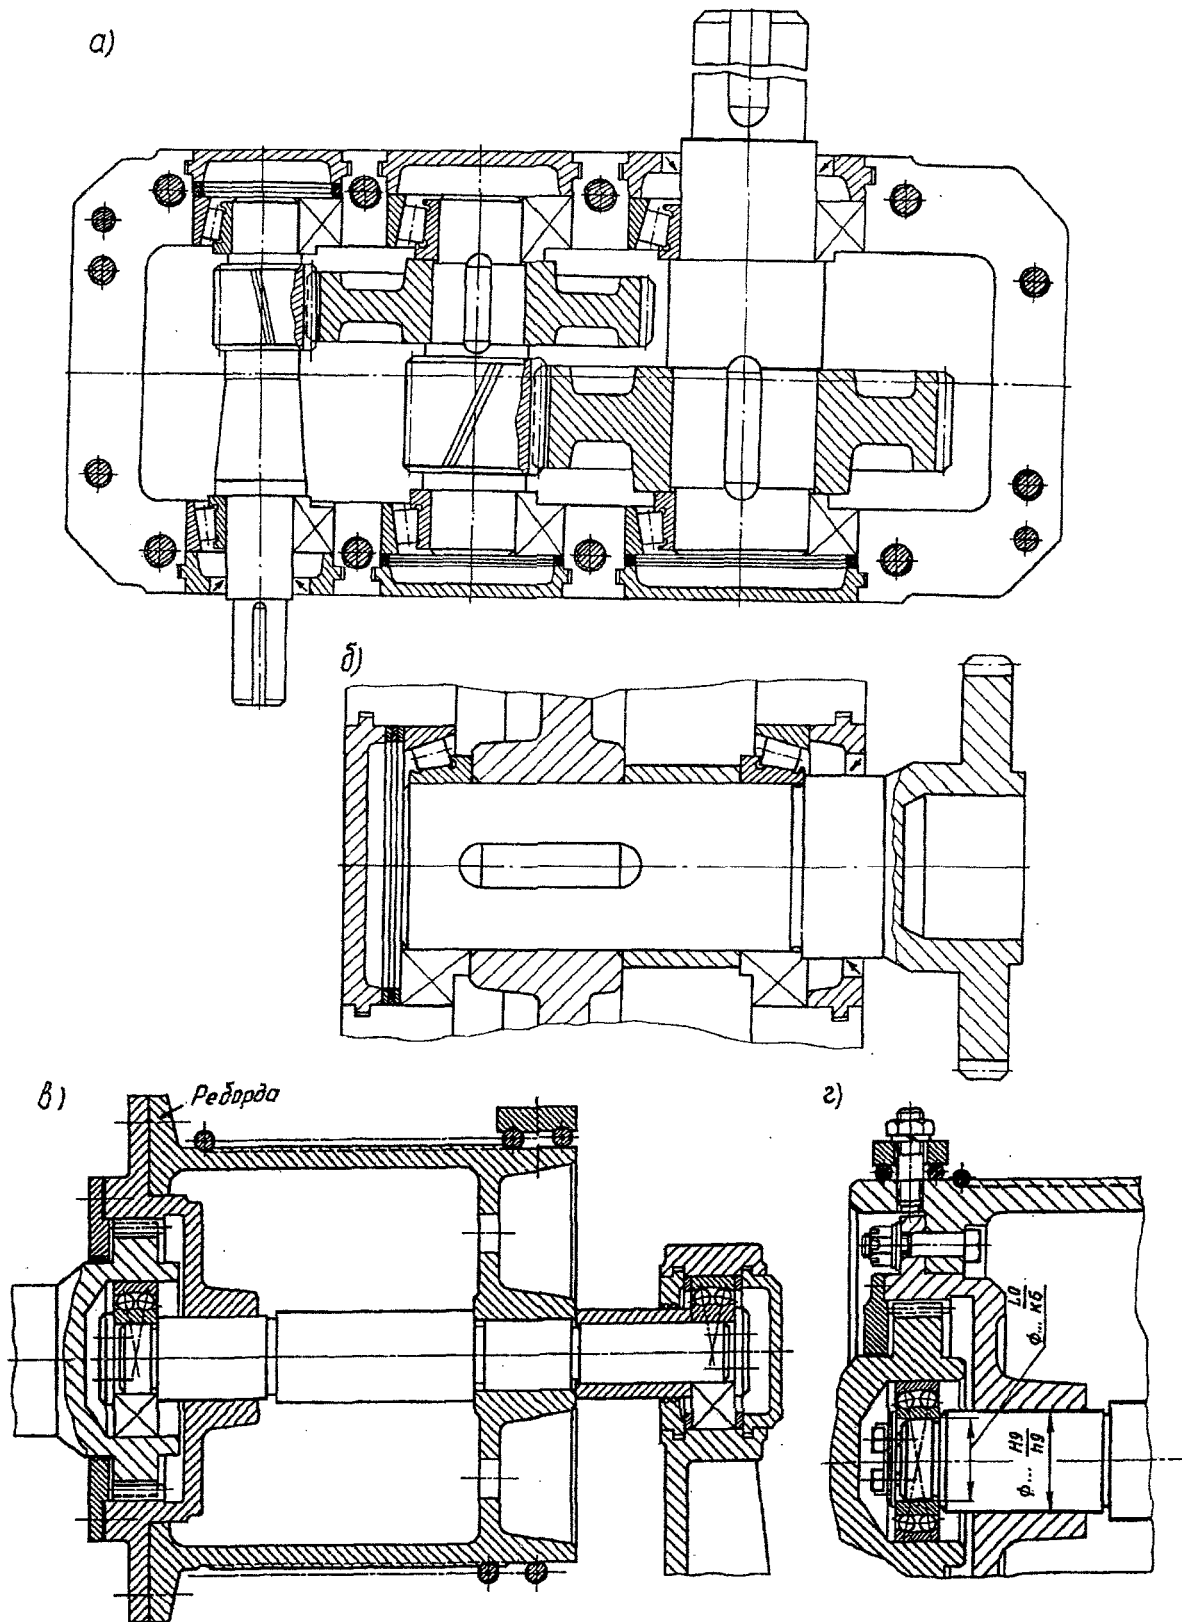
Двухступенчатый цилиндрический горизонтальный редуктор, выполненный по простой развернутой схеме рис. 3.3, а: а – конструкция редуктора; б – тихоходный вал с венцом для зубчатой муфты; в, г – узел барабана со встроенной зубчатой муфтой
